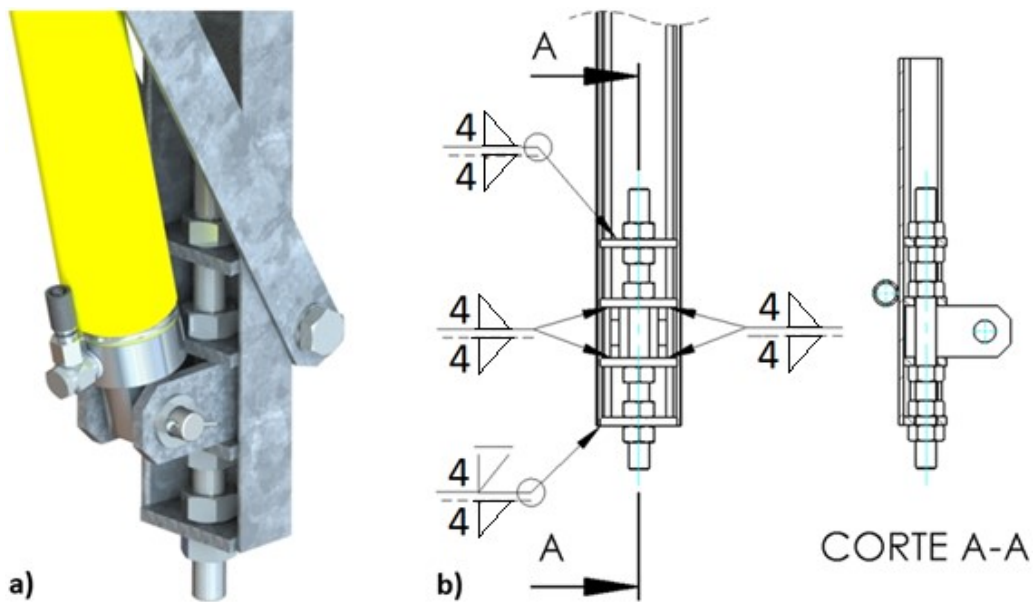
Ligação inferior do cilindro à estrutura: a) perspectiva de montagem, b) representação das soldaduras e vista em corte.
